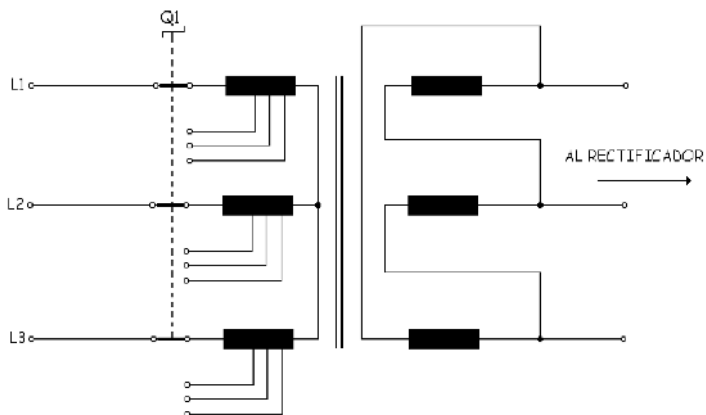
Transformador trifásico de soldadura en conexión Estrella-Triángulo.
